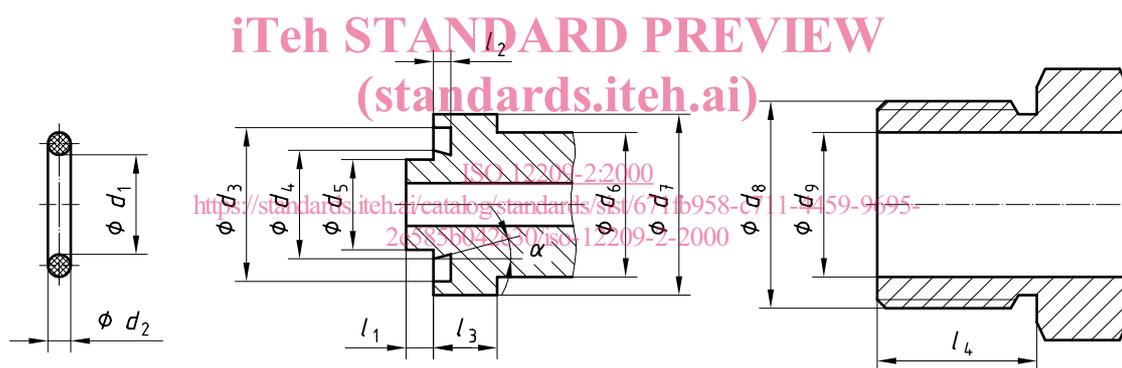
Assemblage de soutirage 300 bar — Éléments
